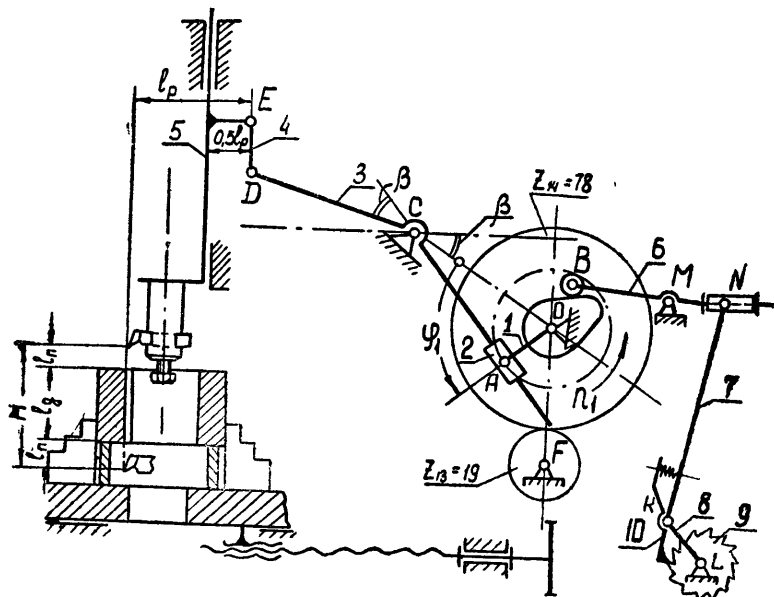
2. Схема кривошипно-кулисного механизма движения резца и кулачкового механизма подачи стола долбежного станка
